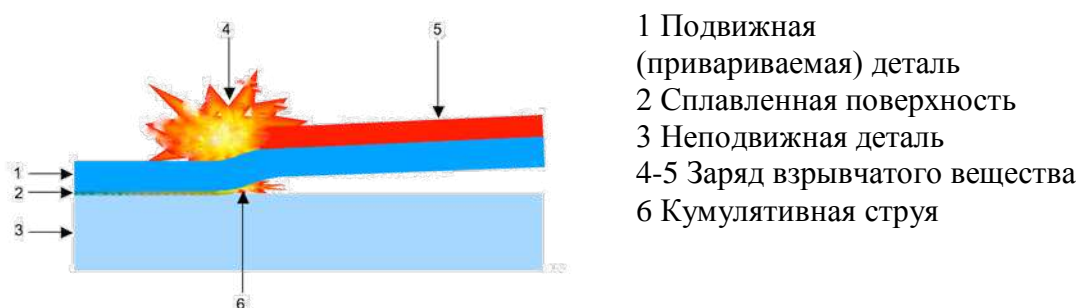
Угловая схема сварки взрывом на стадии взрыва
